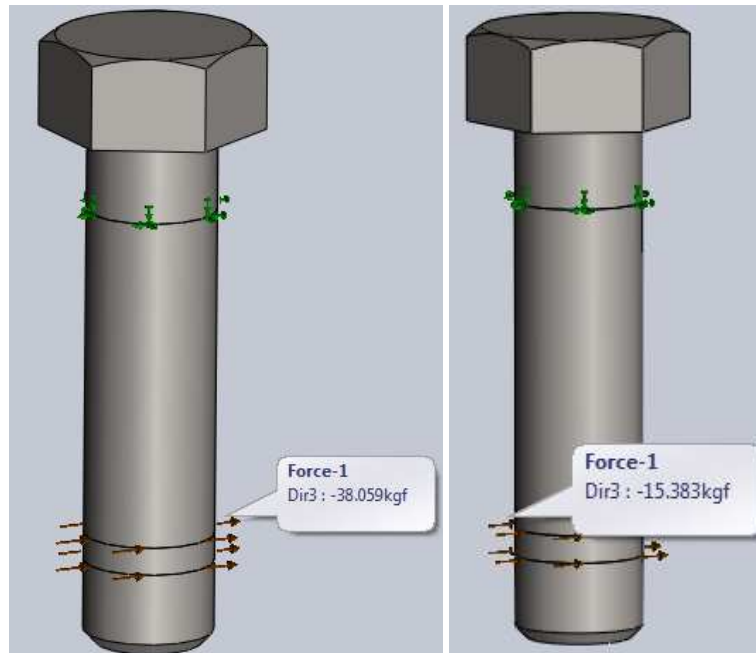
Cargas aplicadas en el eje izquierdo que soporta al resorte a tracción.
